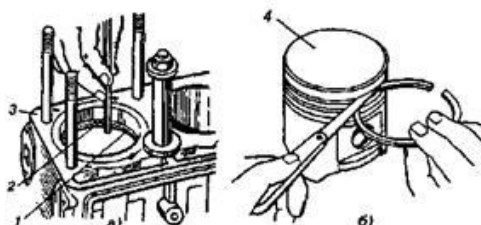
Проверка зазора в замке поршневого кольца (а) и бокового зазора между поршневым кольцом и канавкой в поршне (б): 1 – поршневое кольцо; 2 – шуп; 3 – блок цилиндров двигателя; 4 – поршень
